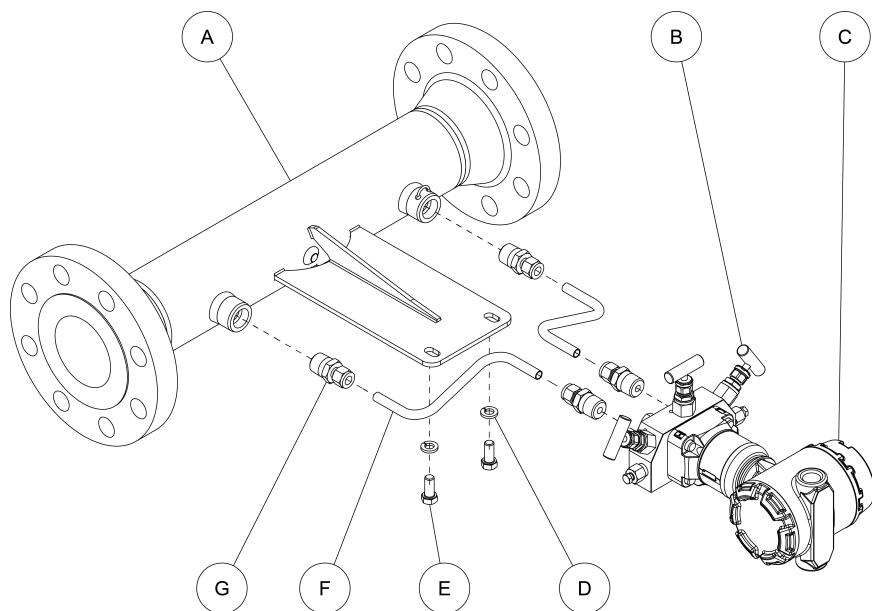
Vue éclatée 2 : Ensemble à bride NPS 2 po/DN50
